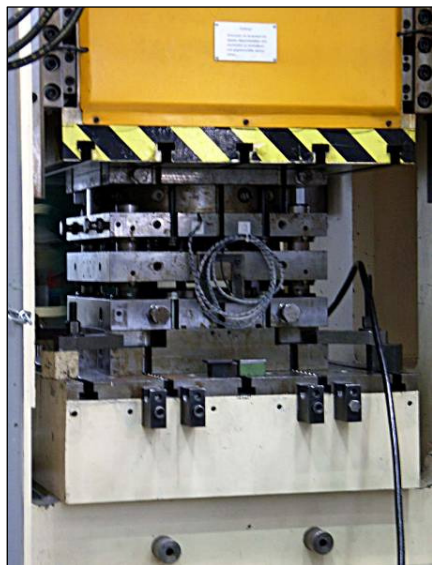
Werkzeug im eingebauten Zustand an der hydraulischen Presse
